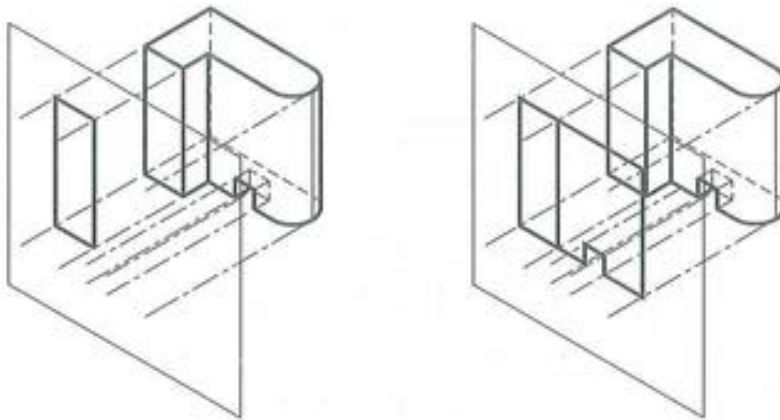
Proyección en el sistema americano donde el plano se interpone entre el foco y la pieza.
